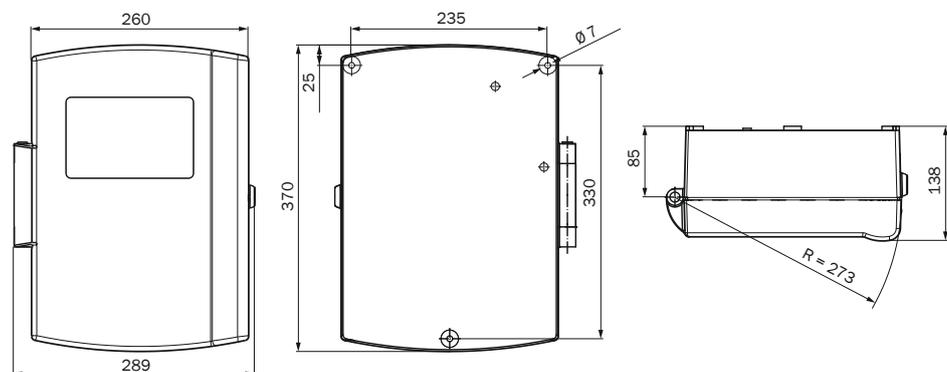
Steuereinheit AWE (Ausführung Metallgussgehäuse), Maße in mm
